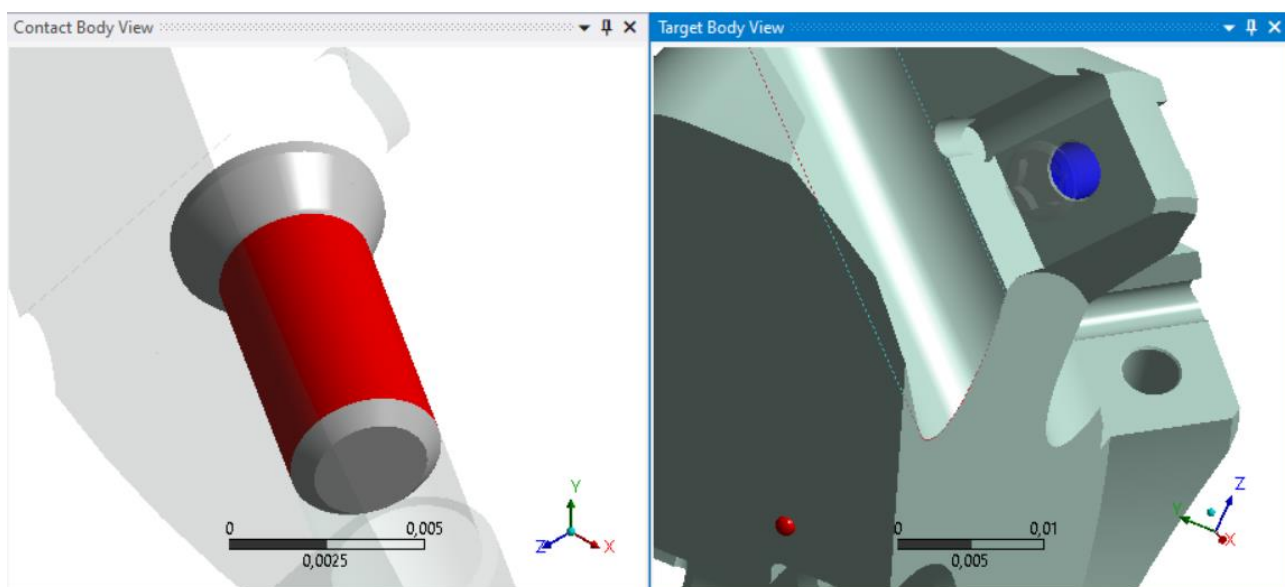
Контакт поверхности винта и отверстия корпуса
